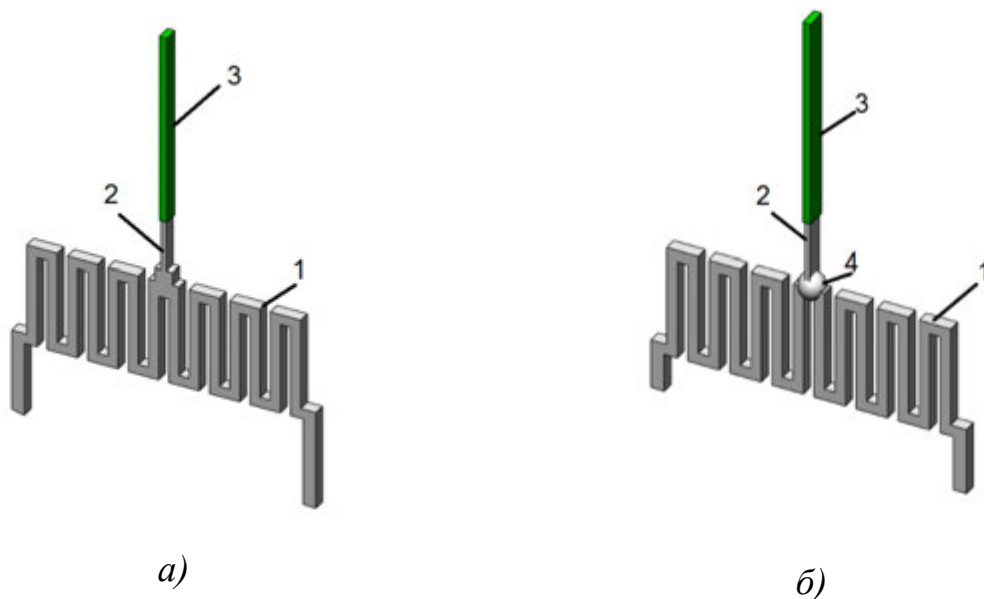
Изображения МНОК изготовленных из фольги сплава ВР-27: в виде цельной детали (а); с присоединением к подогревателю керна лазерной свар-
